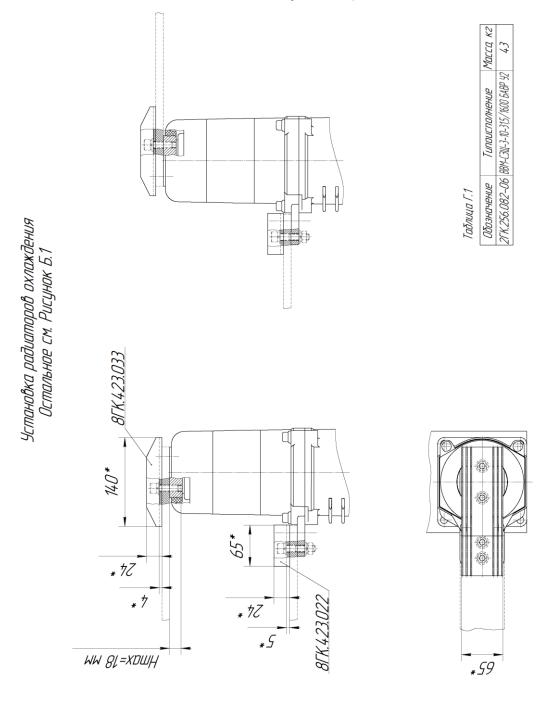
Габаритные, присоединительные и установочные размеры выключателя типа ВВМ-СЭЩ-3-10-31,5/1600 БАВР У2
